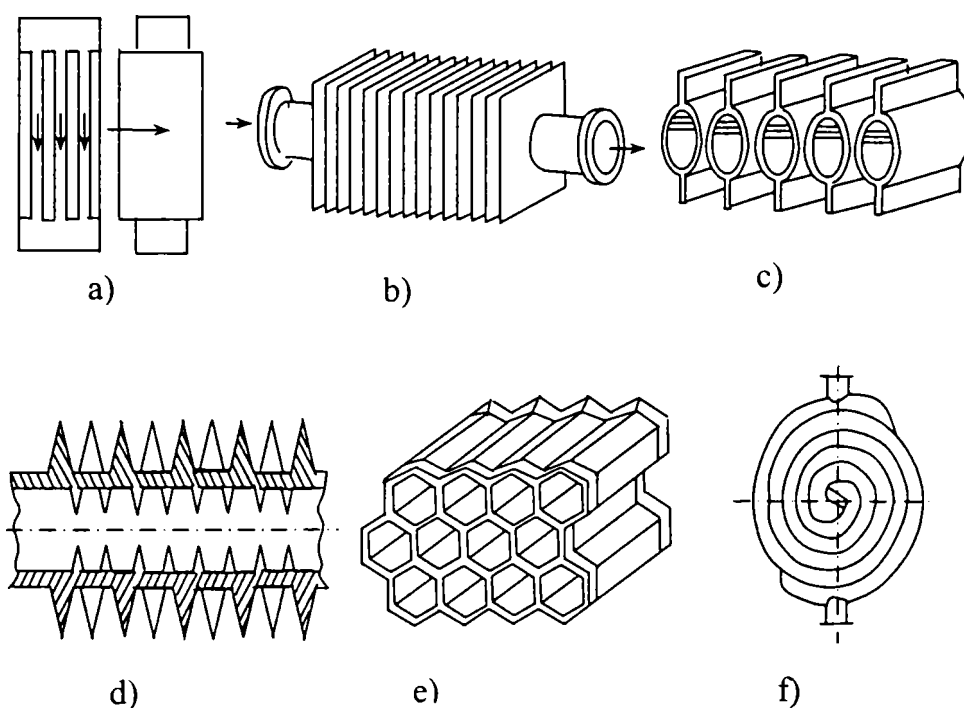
Elemente constructive ale schimbătoarelor de căldură
